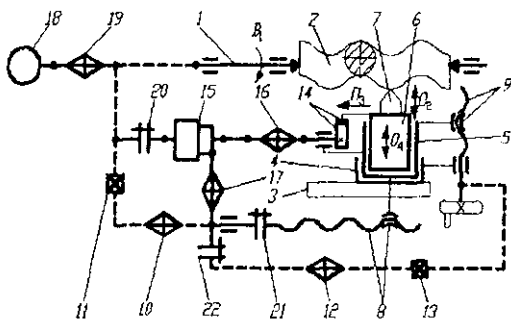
Структурная схема станка для обработки роторов винтовых насосов
